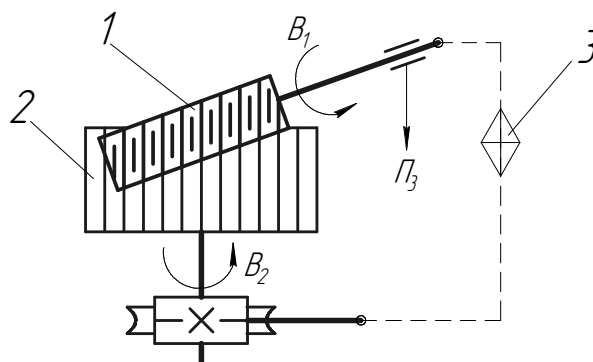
Станочное зацепление червячная фреза – заготовка
